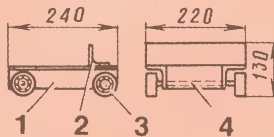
Тележка: 1 — основание; 2 — упор; 3 — колеса (подшипники); 4 — ось.
